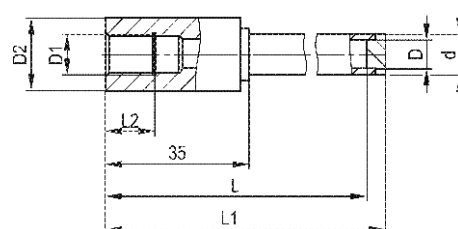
Гильза цилиндрическая резьбовая приварная OG3
